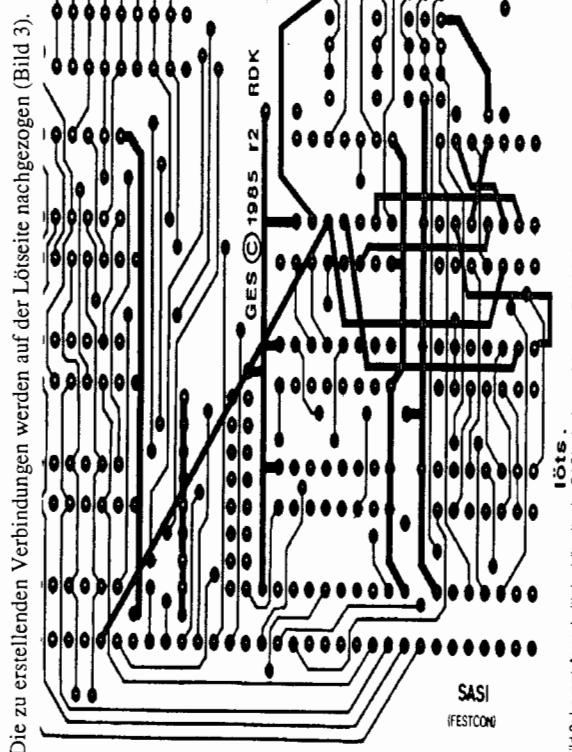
Layout-Ausschnitt der Lötseite der SASI mit eingezeichneten Fädeldrähten
